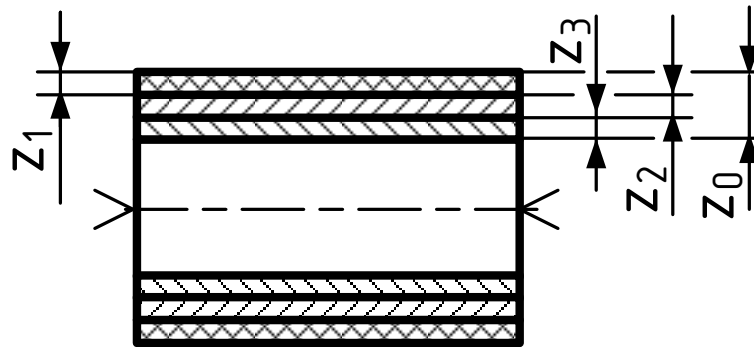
Пример структуры общего припуска при обработке цилиндрической поверхности:
